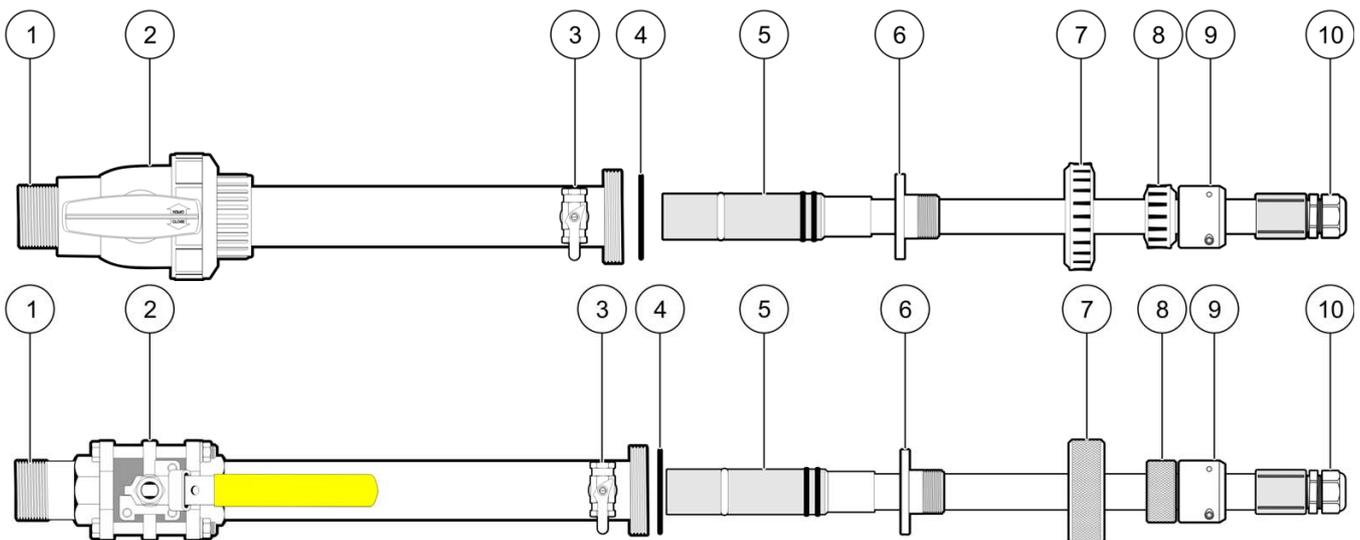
CPVC- und Edelstahl-Rohreinbauarmatur
